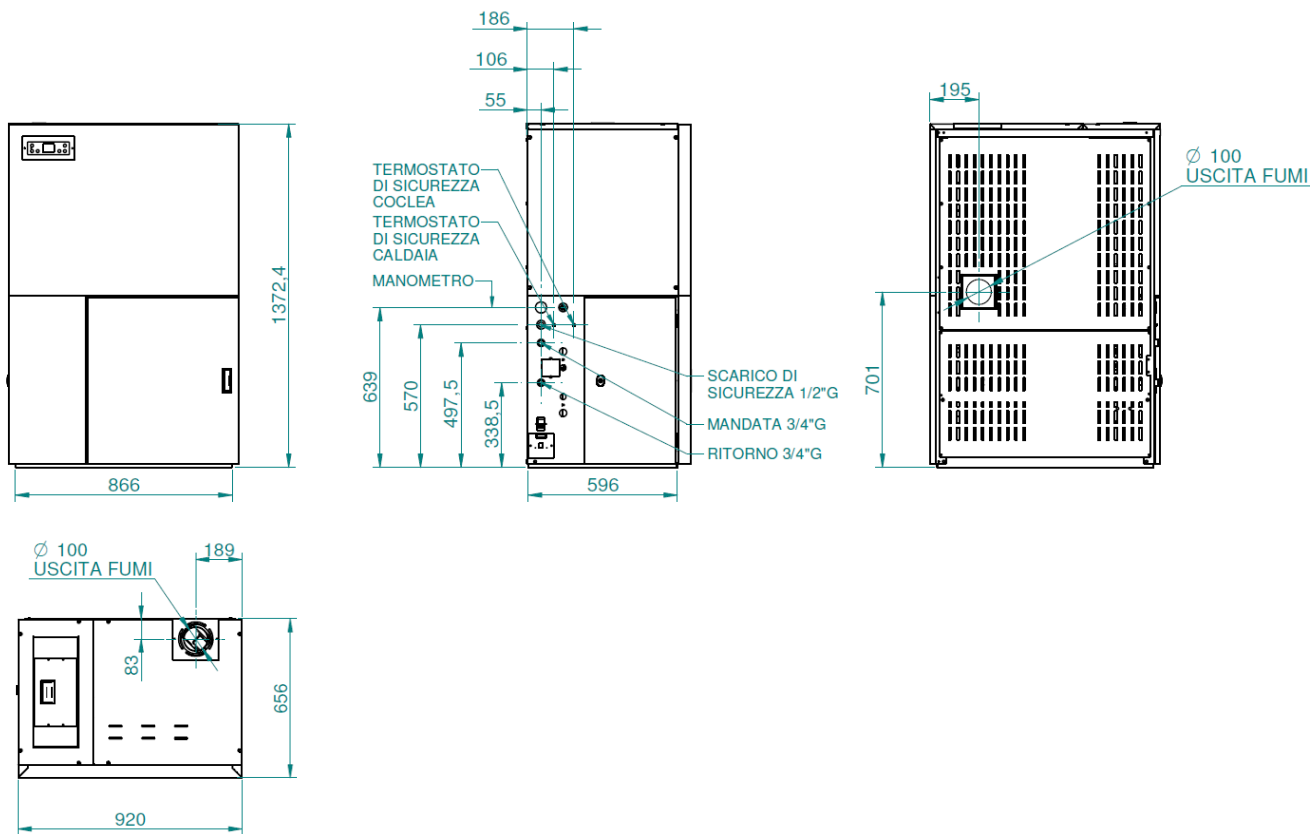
Termo Rodi Advance - dimensioni di ingombro - overall dimensions - dimensions d'encombrement - dimensiones totales
